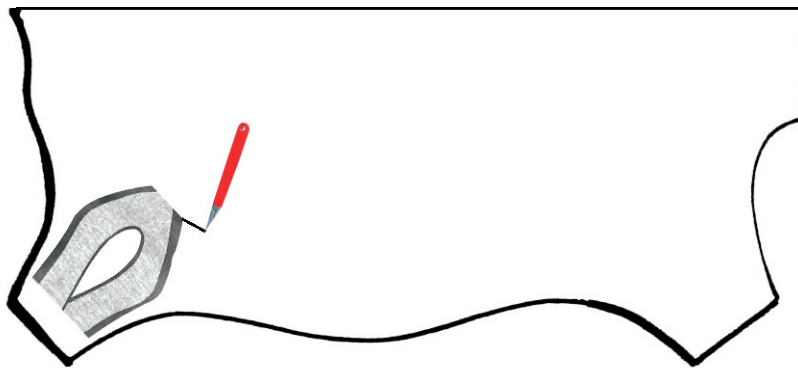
Exemple d'allongement terminal de la coupe à la main.
